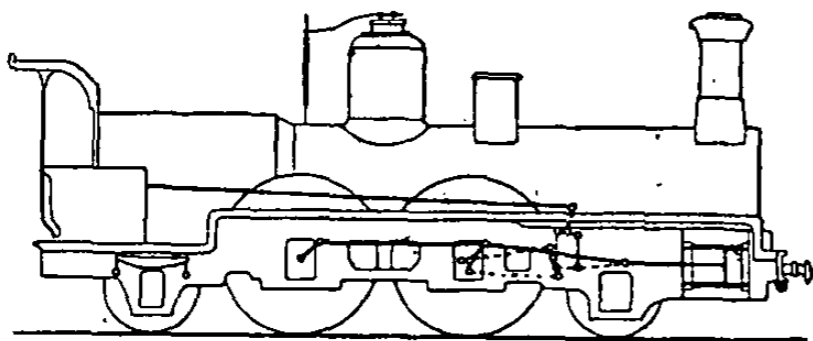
Machine express de la Compagnie P.-L.-M.
